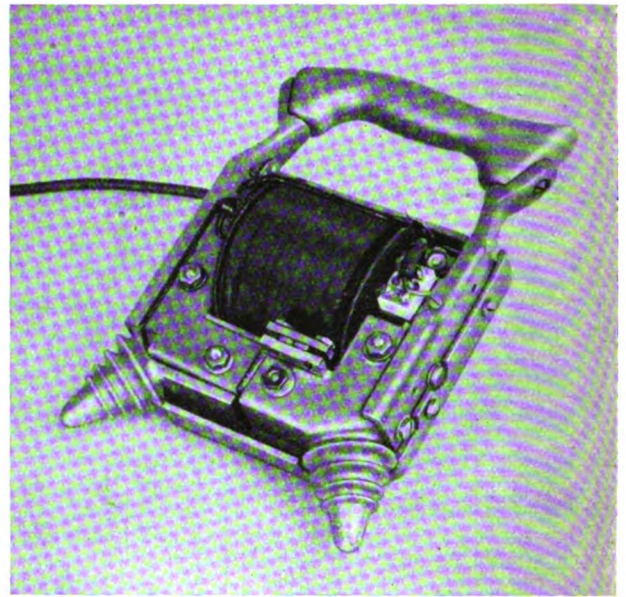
Kleines Handgerät für die Magnetpulverprüfung von Schweißnähten, geöffnet. Hochstromtransformator, Handgriff und Elektroden sind zu einer Einheit verbunden.
